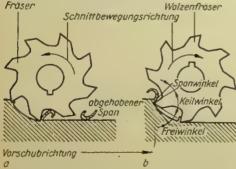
a Gleichlauf- und b Gegenlauffräsen
